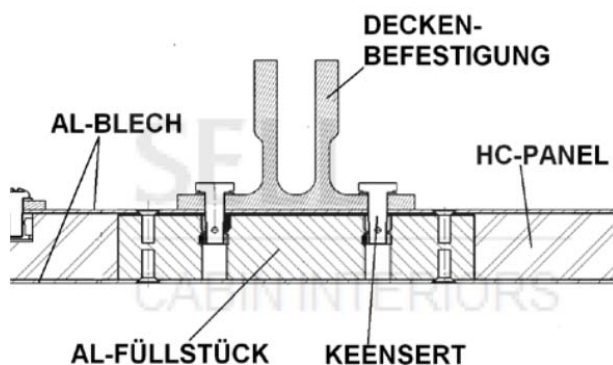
Massiver Aluminiumblock inkl. sog. Keenserts (HeliCoil-Einsätze) als Krafteinleitung (41).
